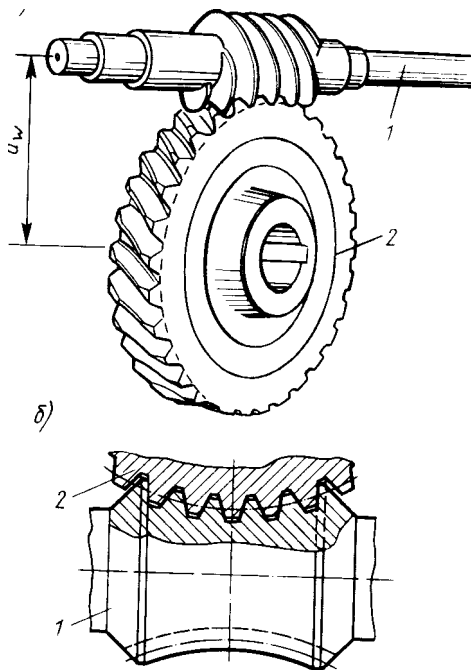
Схема червячных передач: а – обычное зацепление (цилиндрический червяк); б – глобоидное зацепление
